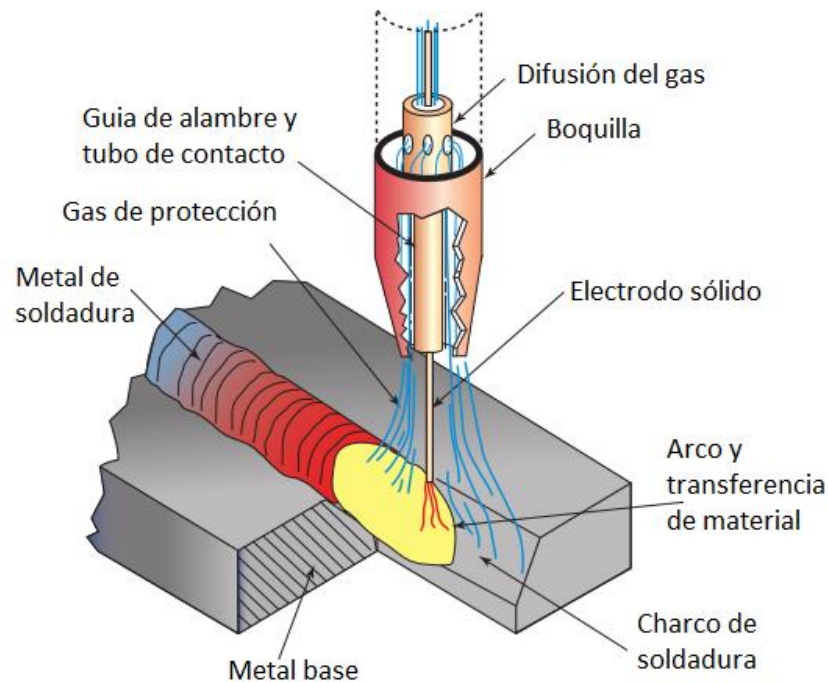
Proceso de soldadura GMAW [3].
